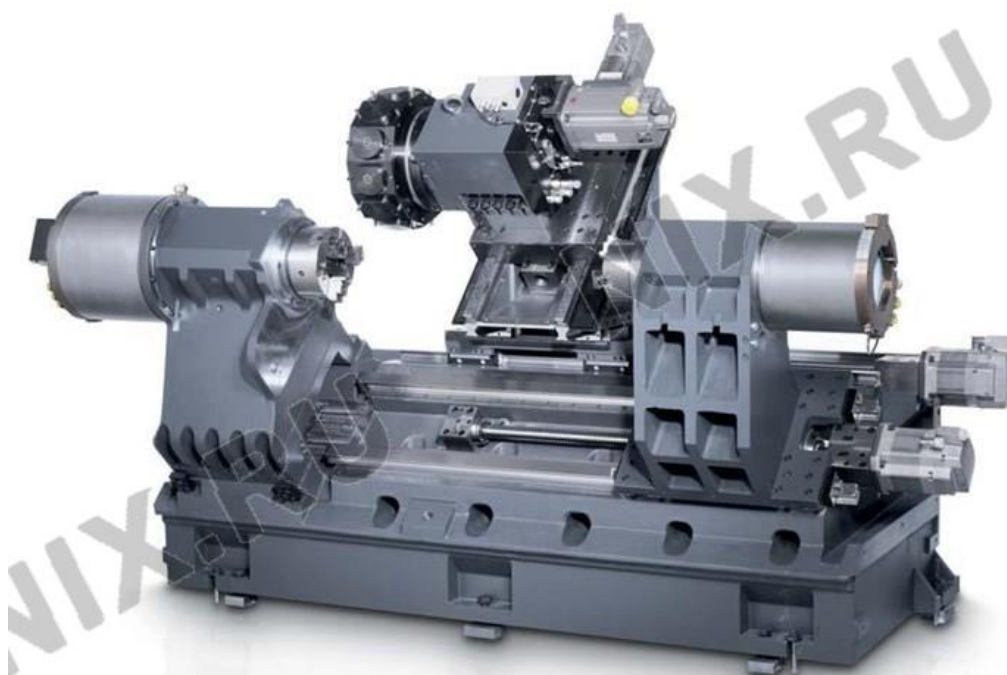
Компоновка токарного центра с ЧПУ СТХ ВЕТА 800
